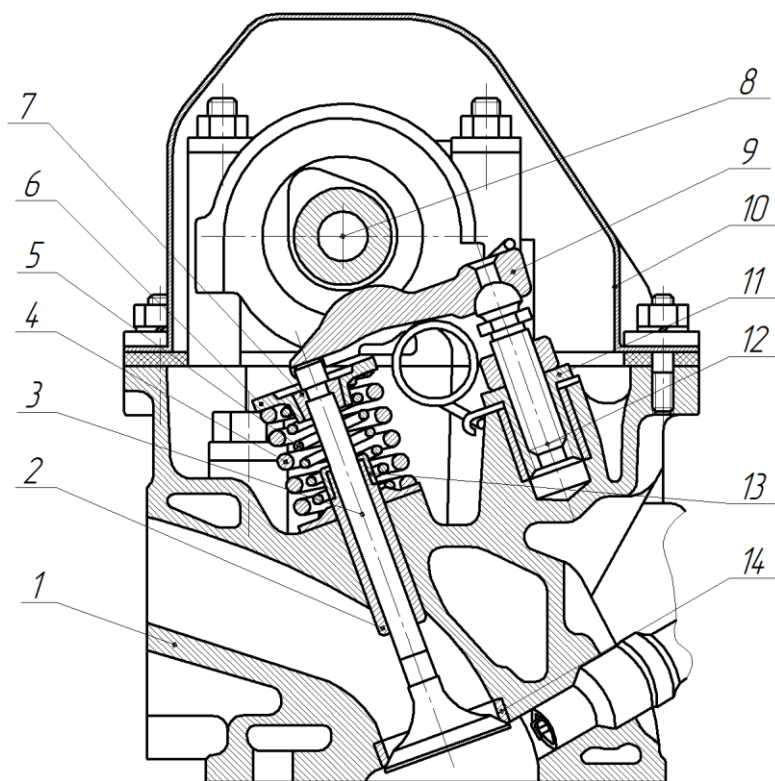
Газораспределительный механизм типа ОНС:
